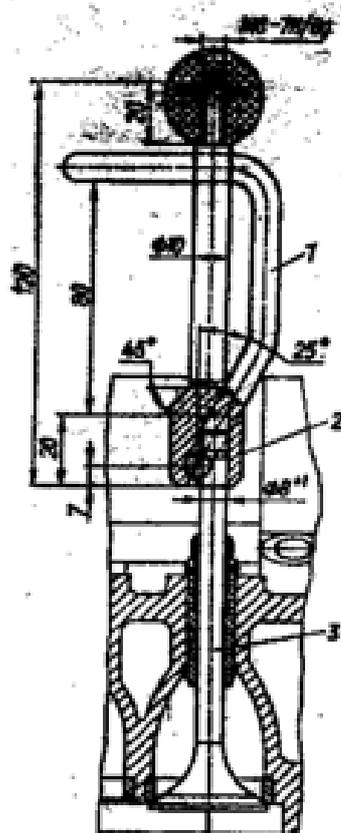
Приспособление для притирки клапанов М9849-120: 1 - зажим; 2 - оправка; 3 - клапан
